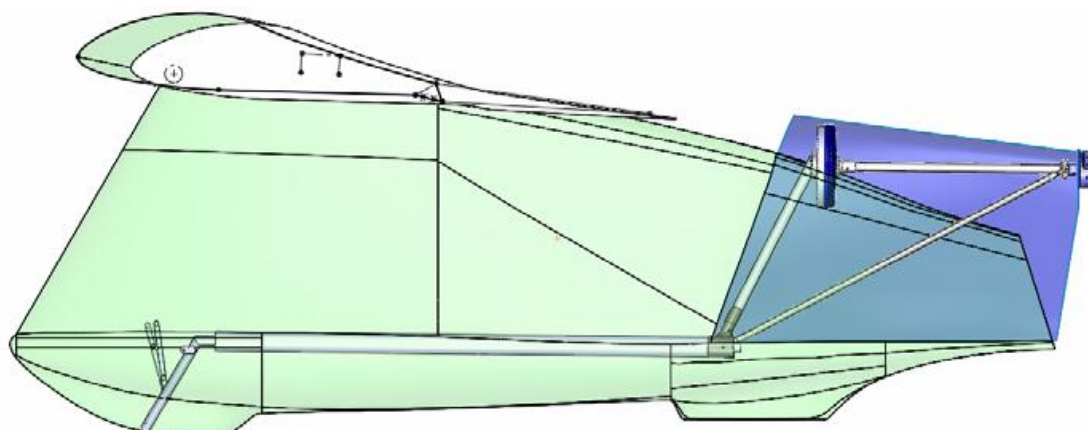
Desenho CAD Esquemático da Nova Carenagem Traseira
